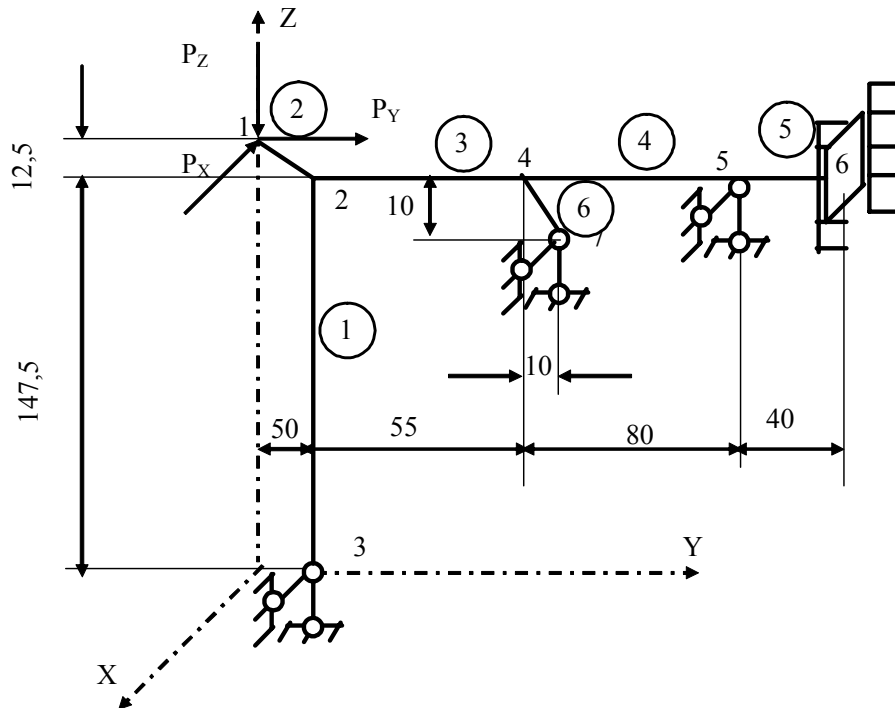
Расчетная схема сборного резца с винтовым креплением
